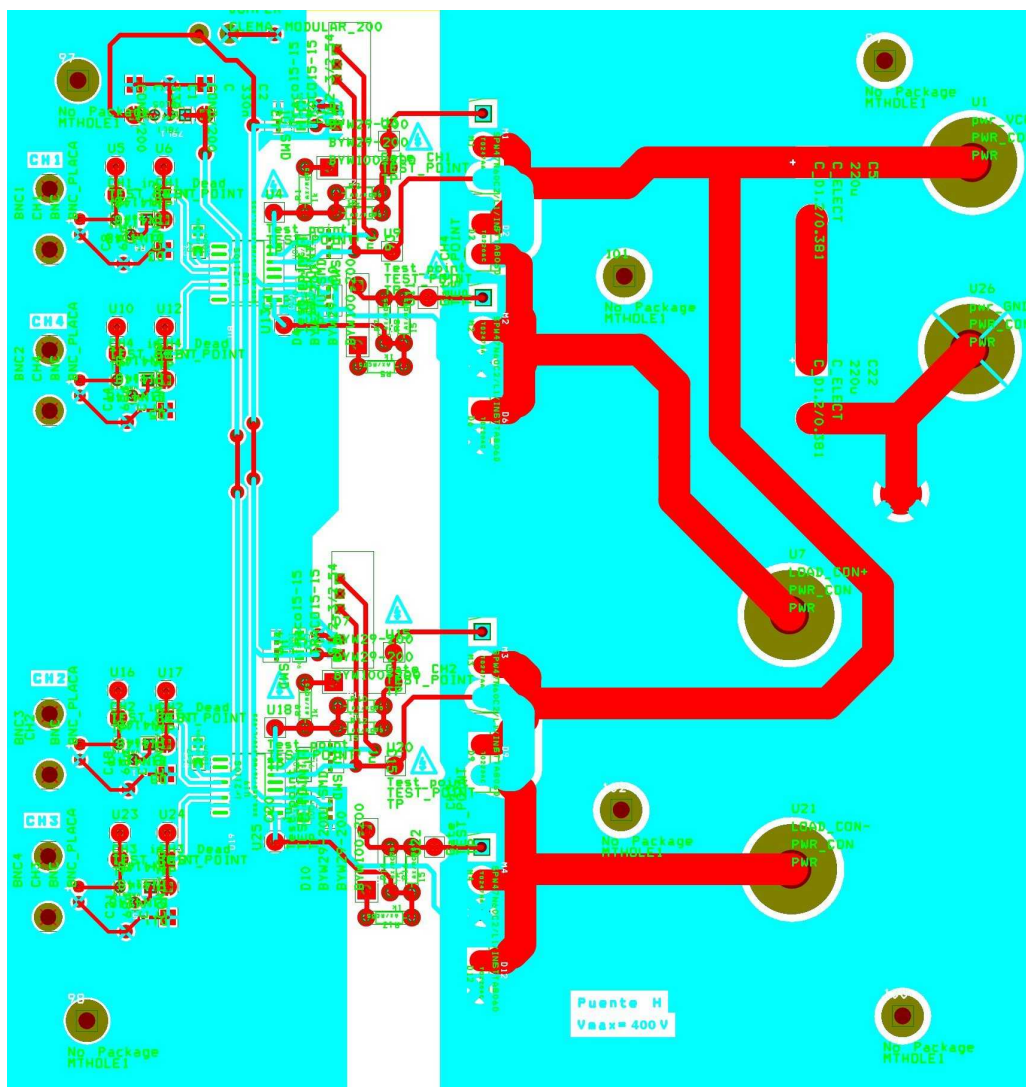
Layout de la PCB de la tarjeta puente completo.
